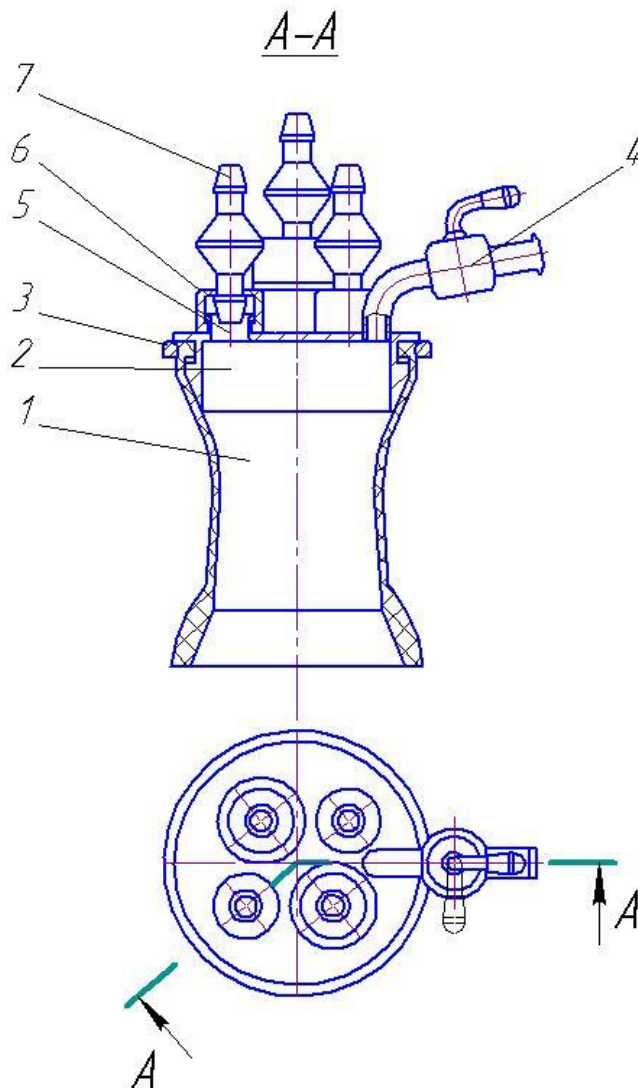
Троакар для единого лапароскопического доступа с инструментальными каналами, с газоподачей.
